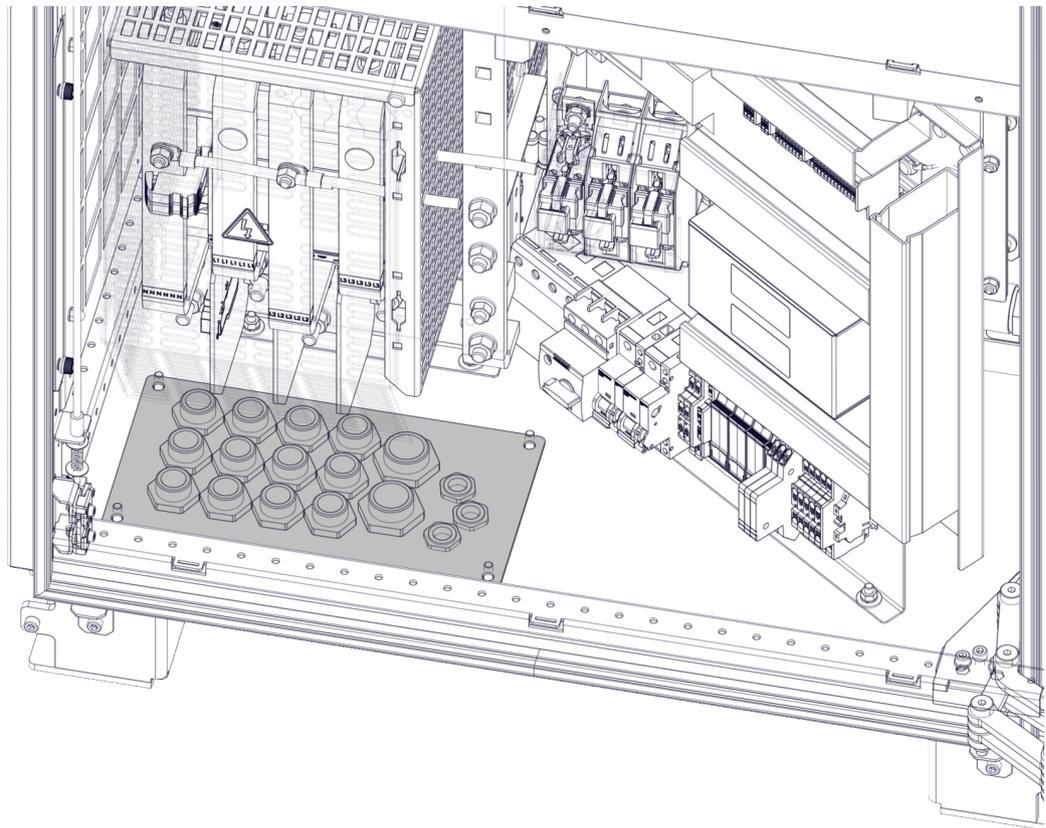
Kabeldurchführungsplatte für das Netzkabel
